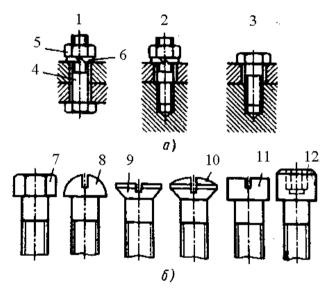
Типы резьбовых соединений (а) и формы головок (б): 1 – болтом; 2 – шпилькой; 3 – винтом; 4 – болт; 5 – гайка; 6 – шайба; 7 – шестигранная; 8 – полукруглая; 9 – потайная; 10 – полупотайная; 11 – цилиндрическая; 12 – цилиндрическая с углублением под шестигранный ключ
